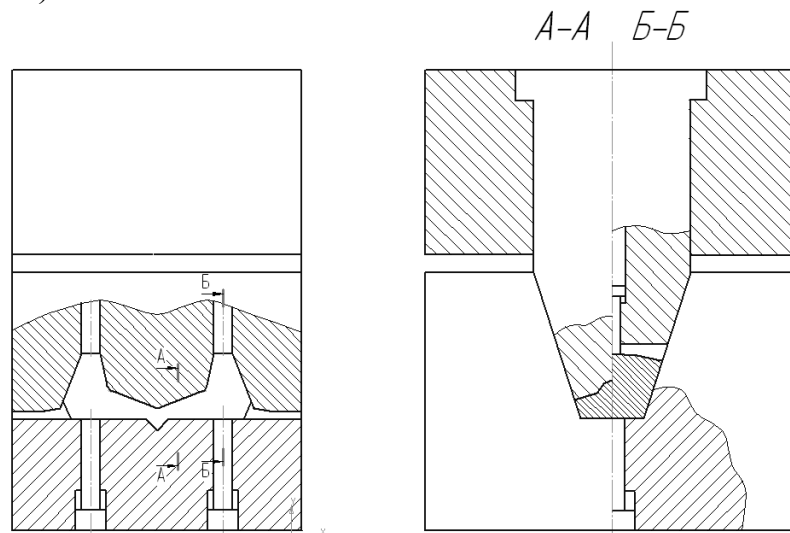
Схема перетискного рівчака КГШП для виготовлення сухаря
